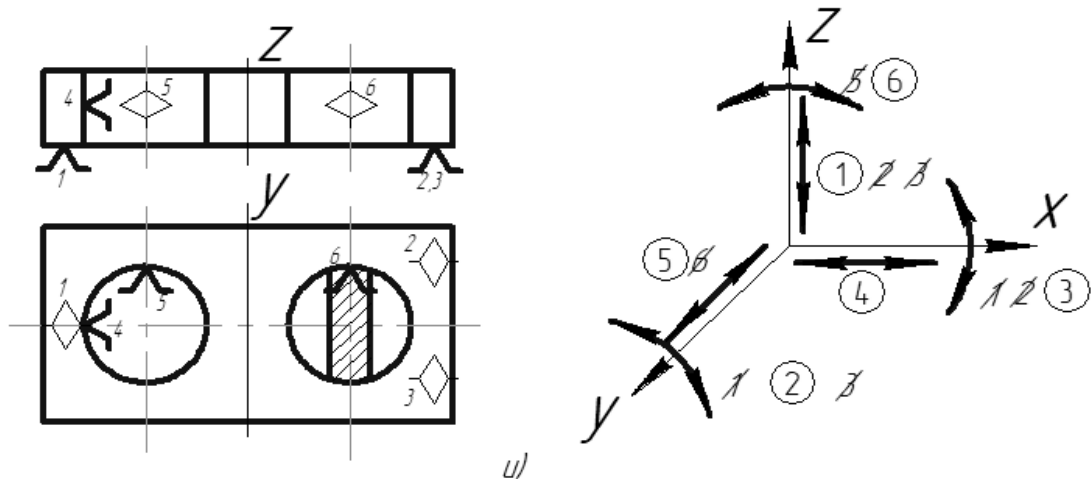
Базування призматичної заготовки по площині та двома пальцями
